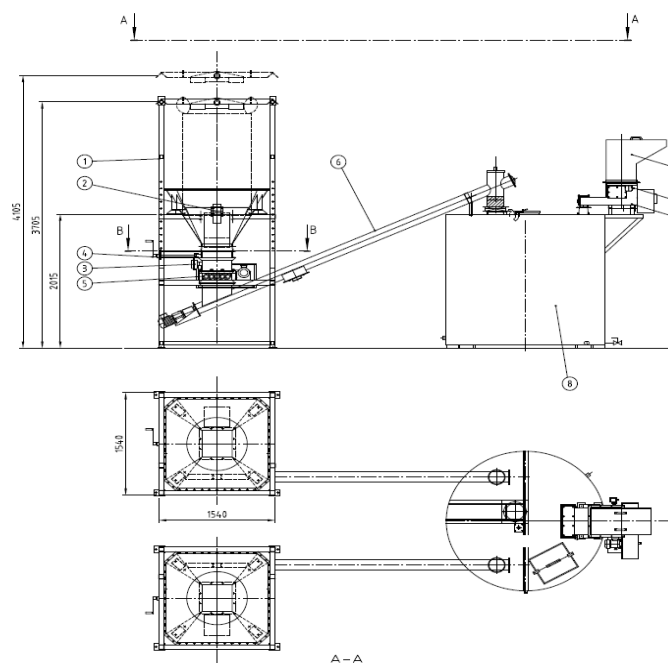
Габаритный чертеж установки приготовления трехкомпонентного раствора
